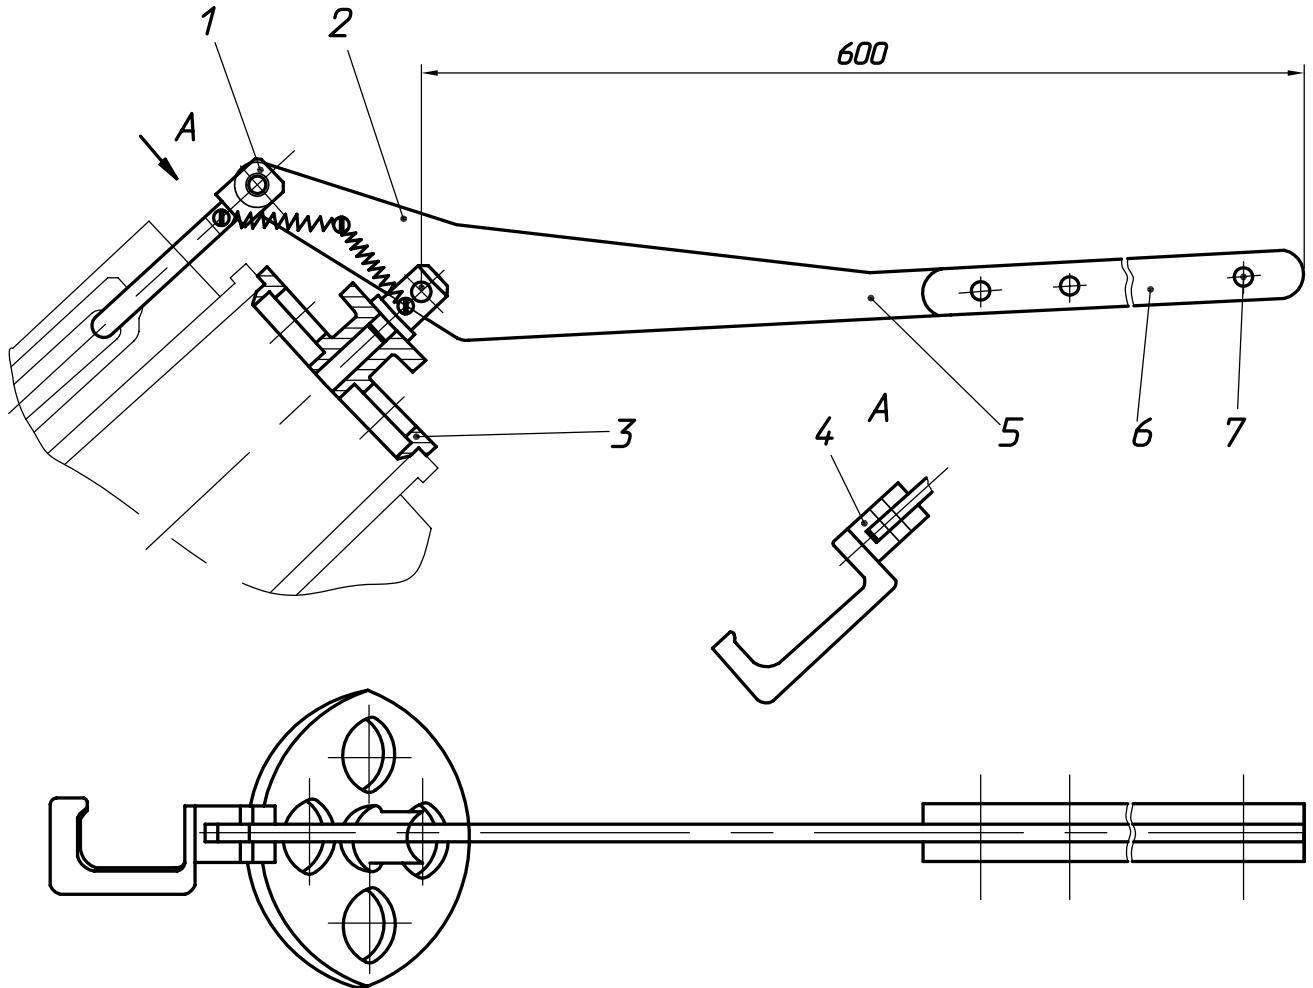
Приспособление для запрессовки гильз в цилиндр
